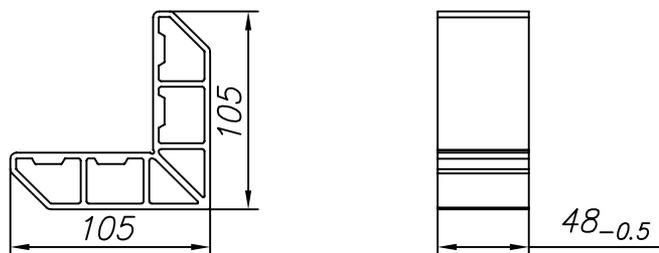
Изготовление соединителя углового FLGU.400.0910
